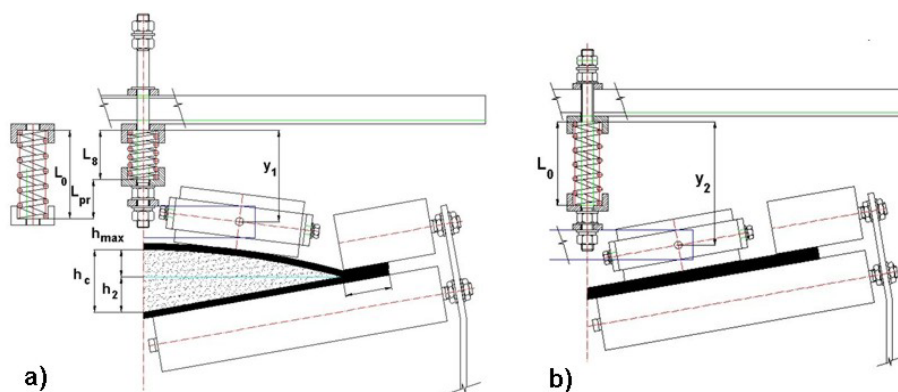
Přítlačný mechanismus krycího pásu realizovaný tlačnou válcovou pružinou v řezu
